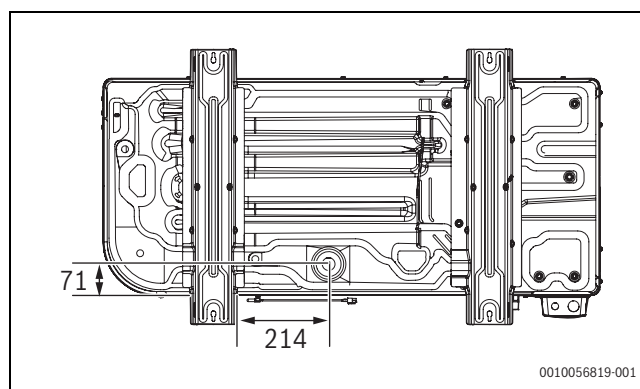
Dimensions de la pompe à chaleur, vue de dessous
